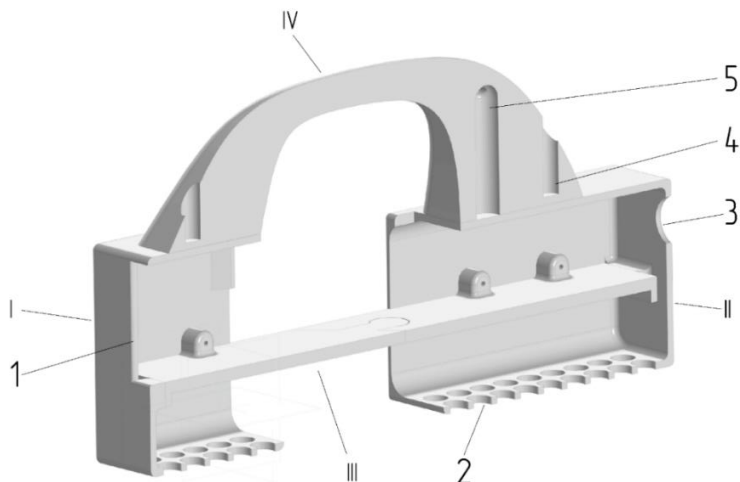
Конструкция корпуса блока управления:
